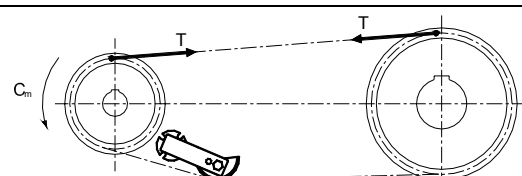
MONTAGGIO CORRETTO / CORRECT ASSEMBLY / KORREKTE MONTAGE
